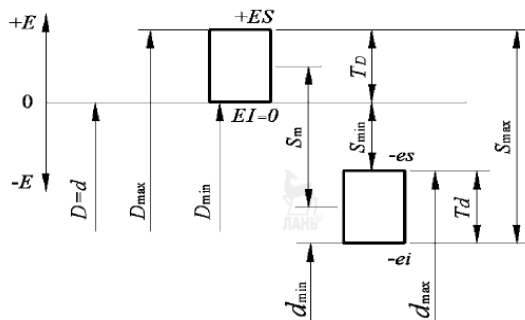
Схема расположения интервалов допуска посадок с зазором
